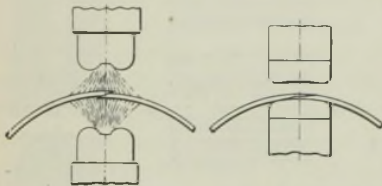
Schweißen des Rohres nach dem Wassergasschweißverfahren.
